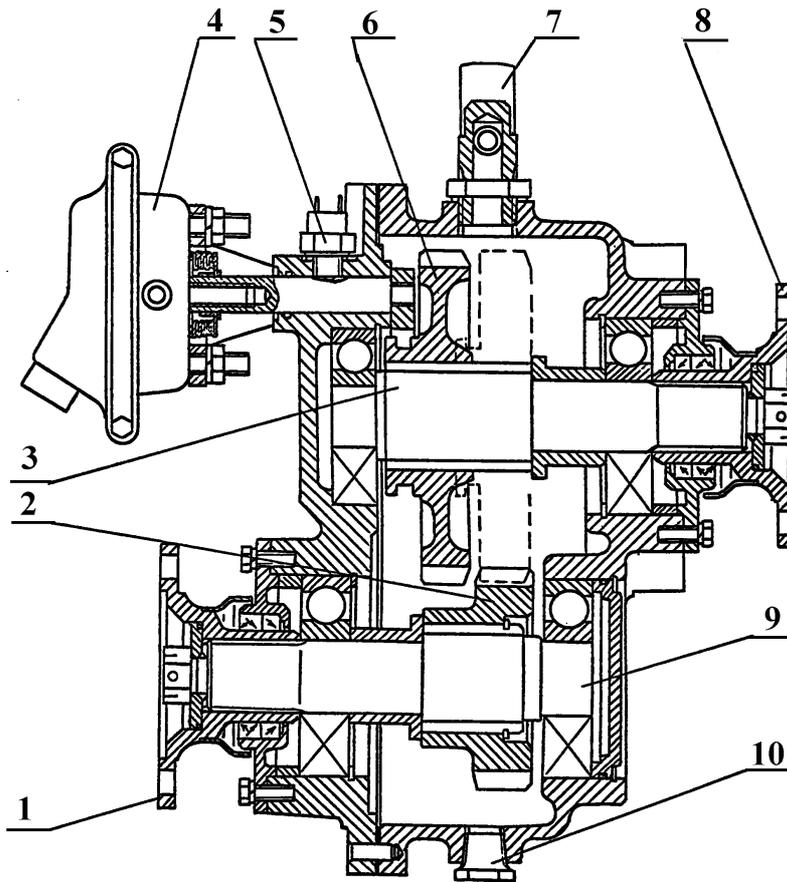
Редуктор: 1, 8 – фланцы; 2, 6 – шестерни; 3, 9 – валы; 4 – пневмокамера; 5 – выключатель; 7 – заправочная горловина; 10 – сливная пробка; 11 – контрольная пробка
